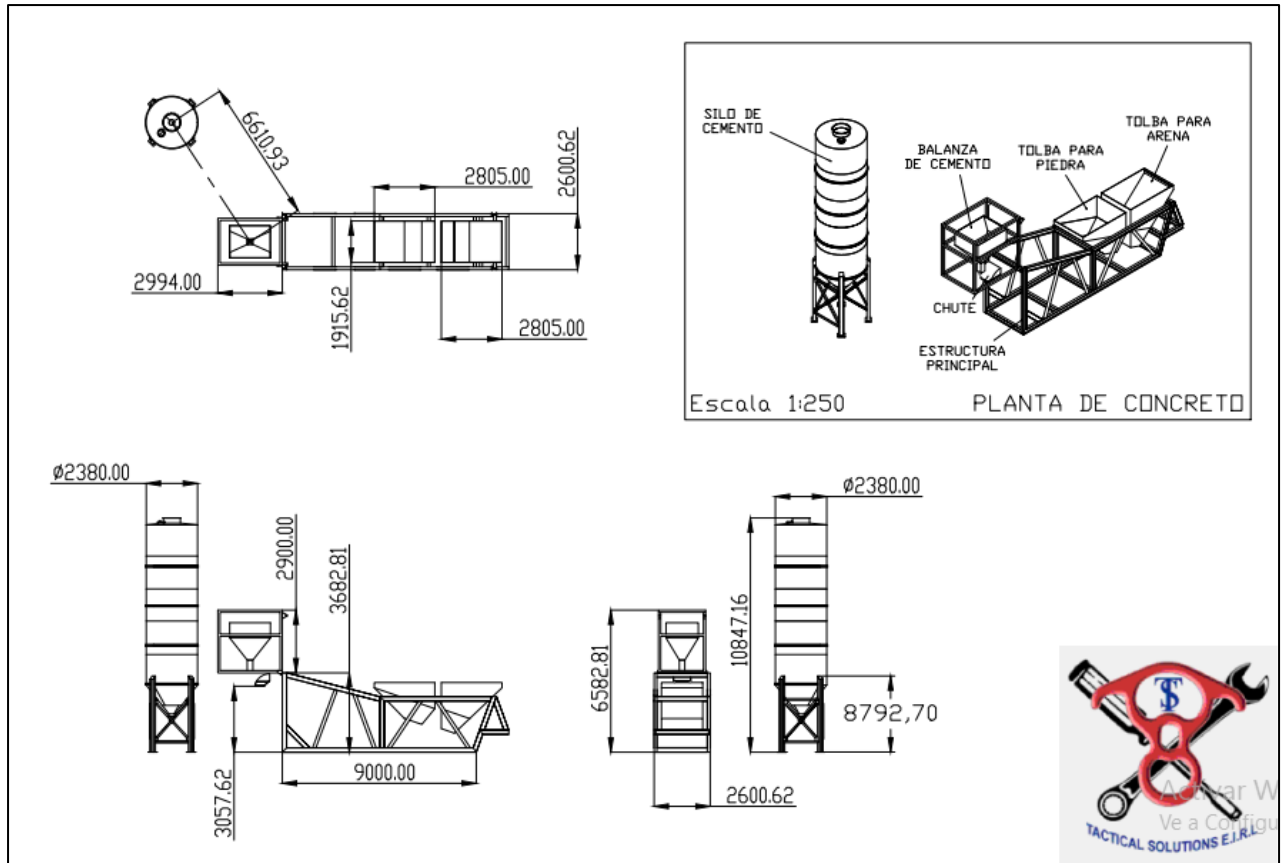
Plano mecánico de distribución de planta dosificadora. Fuente: Elaboración propia (2020).
